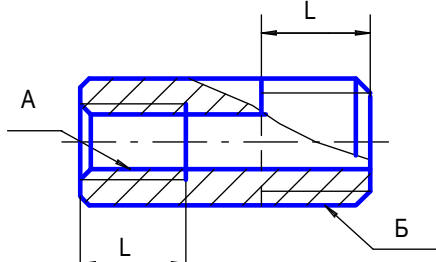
Пример изображения и обозначения метрической резьбы
